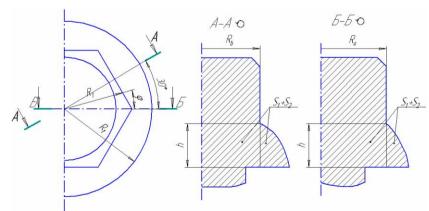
Заготовка болта с фланцем после редуцирования шестигранной головки в пуансоне с вогнутой деформирующей частью
